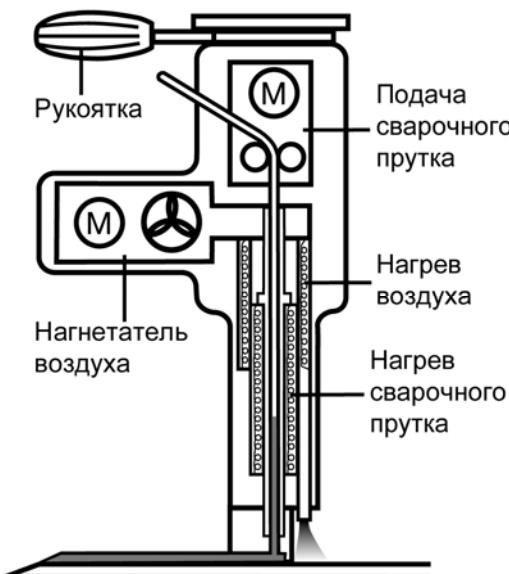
Схема работы сварочного экструдера плунжерного типа
